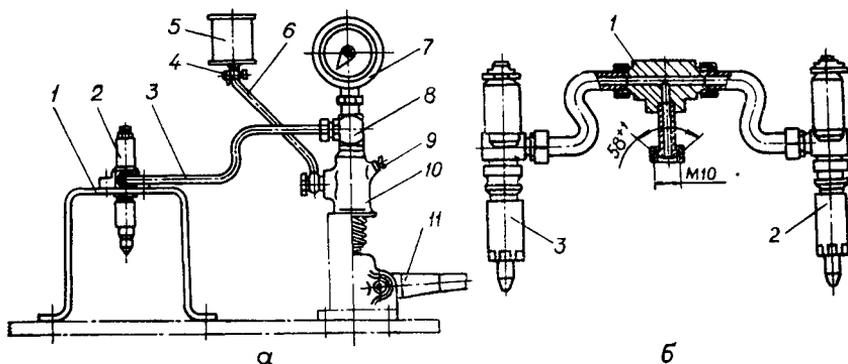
Схемы установки приспособлений для проверки форсунок:
